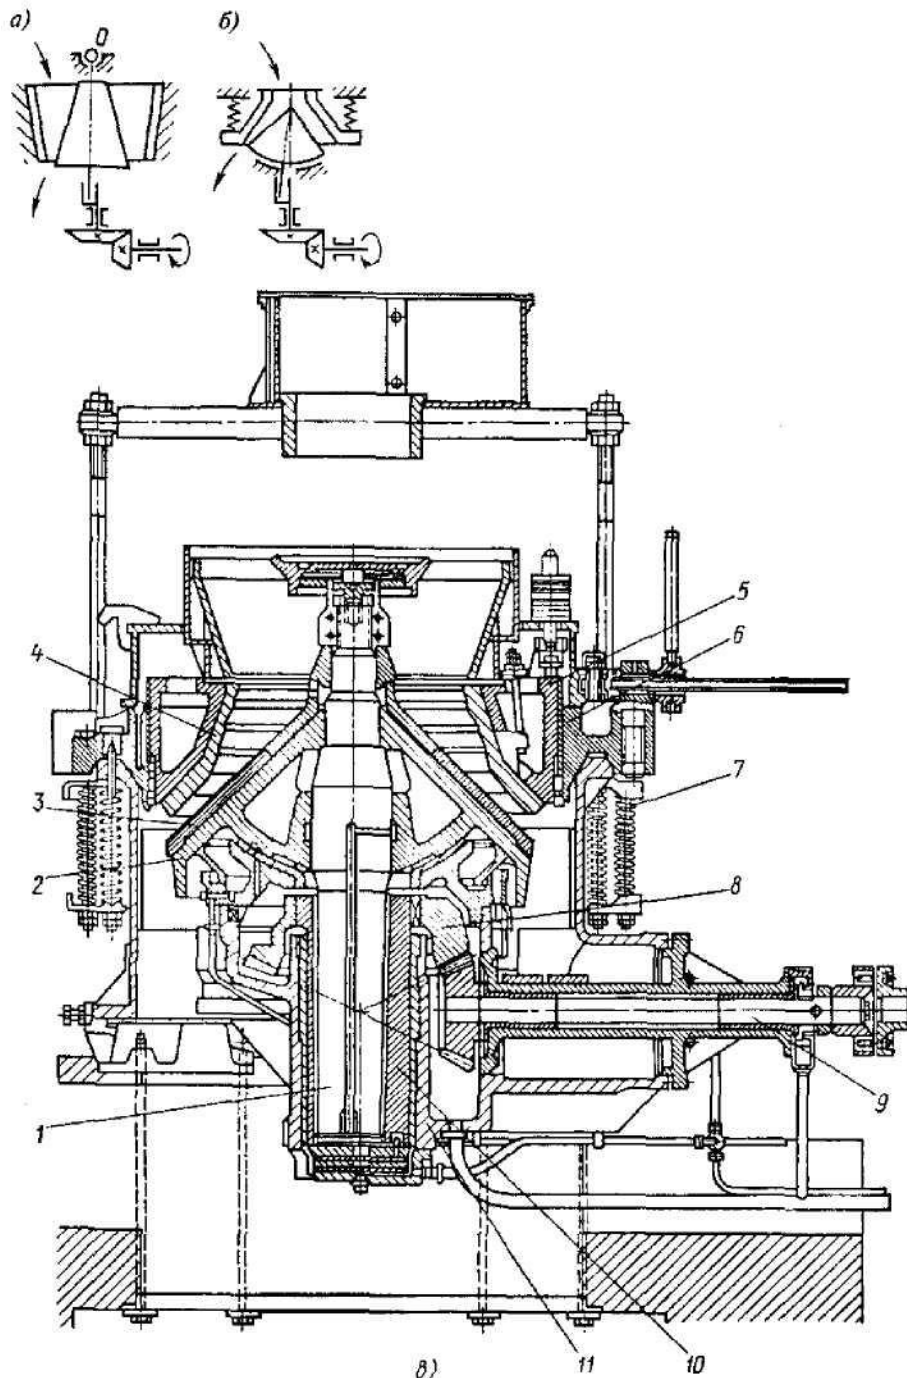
Схема конусных дробилок крупного (а), среднего и мелкого (б) дробления; конструкция дробилки среднего дробления с опорой подвижного конуса на подшипник качения (в): 1 - консольный вал; 2 - корпус конуса; 3 - дробящий конус; 4 - сменный неподвижный дробящий конус; 5 - корпус неподвижного конуса; 6 - опорное кольцо; 7 - прижимные и предохранительные пружины; 8 - коническая шестерня; 9 - приводной вал; 10 - эксцентриковая втулка; 11 - эксцентриковый стакан
